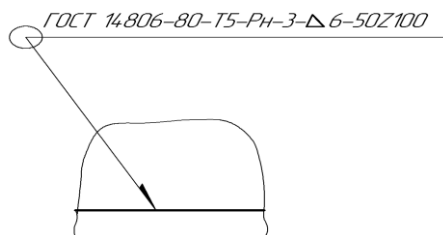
Условное обозначение таврового сварного шва
